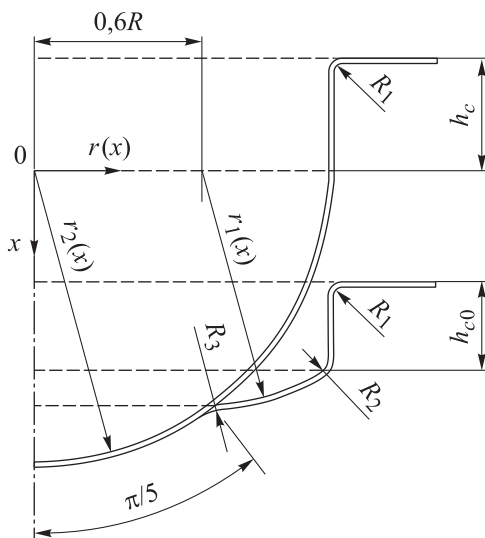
Образующие заготовки для ротационной вытяжки и готового кожуха
